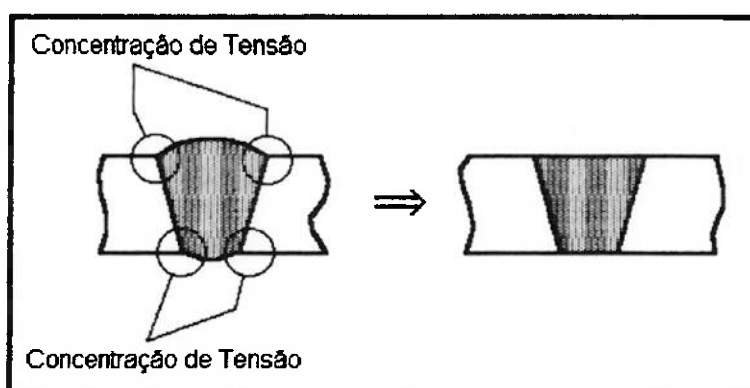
Acabamento final do cordão de solda de penetração total
